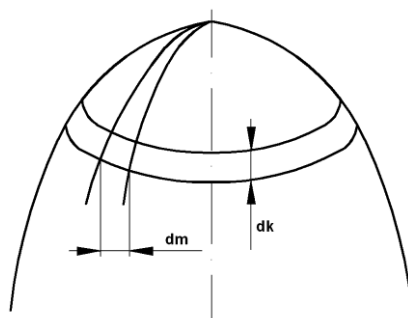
Zkouška rozšiřováním otvoru podle Siebela a Pompa
